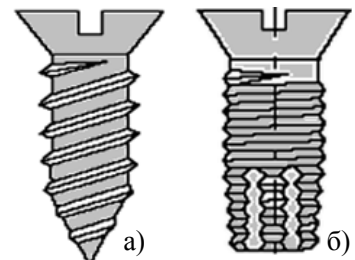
Самонарізні гвинти: а – формувальний; б – різальний
